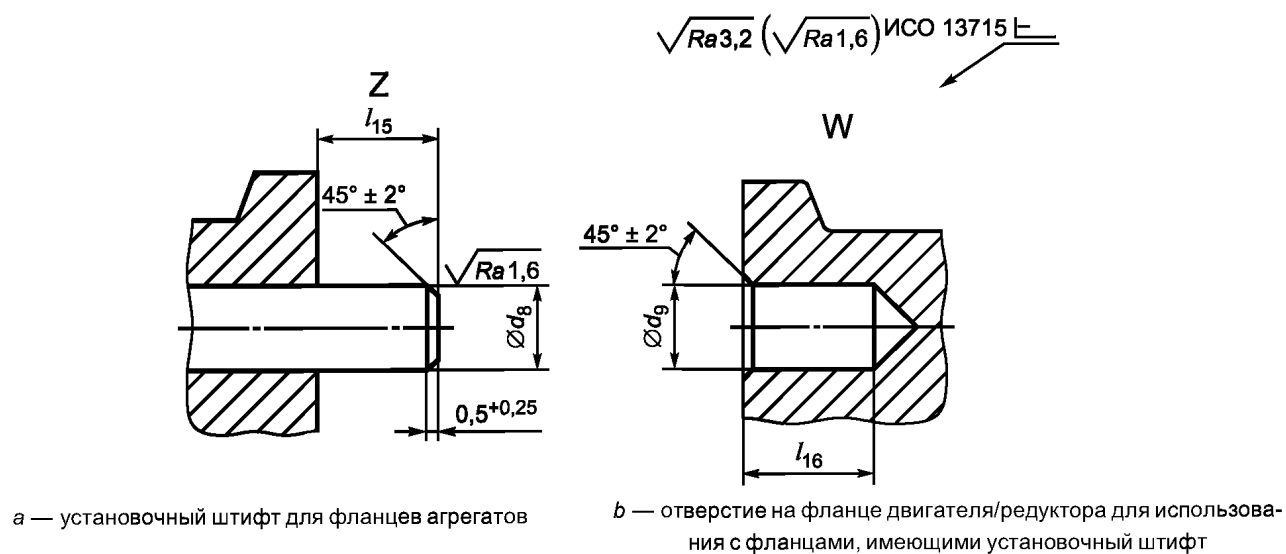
Конструкция и размеры для фланцев агрегатов и фланцев двигателя/редуктора с установочными штифтами
